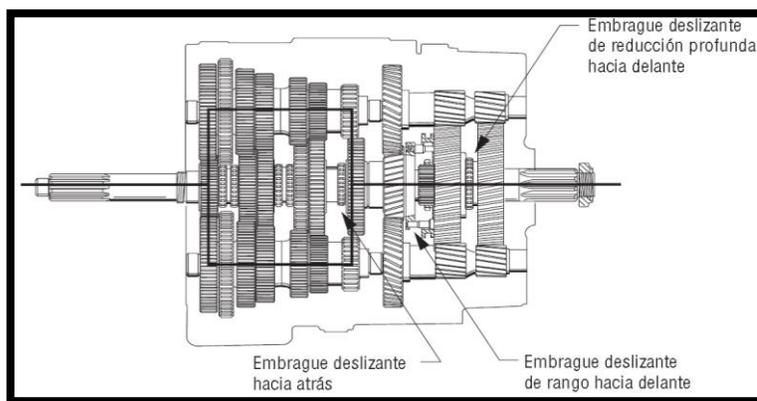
Engrane de reversa, transmisión tráiler: Fuente [34]
